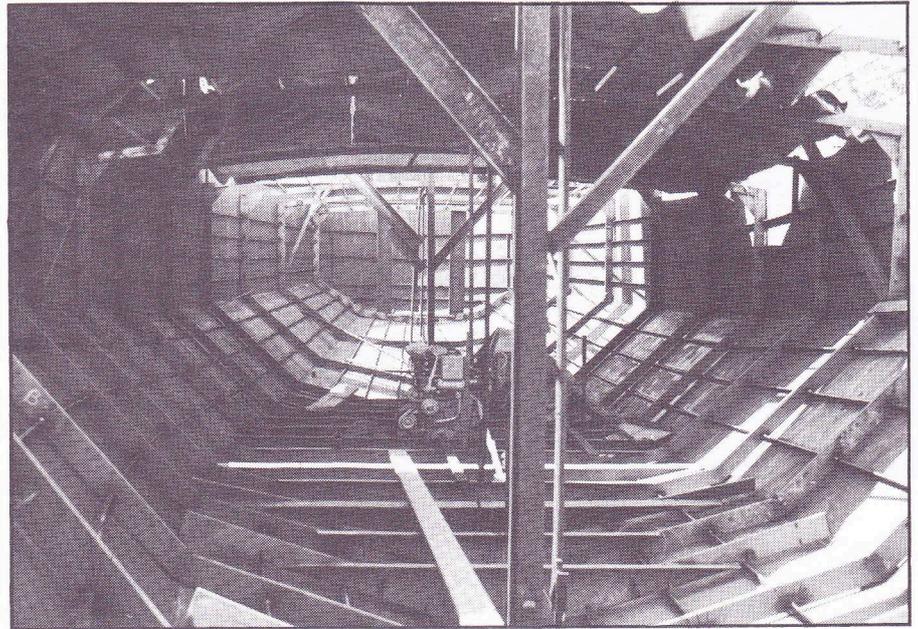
Ensemble de structure sur lisses. (Photo Lardy).
